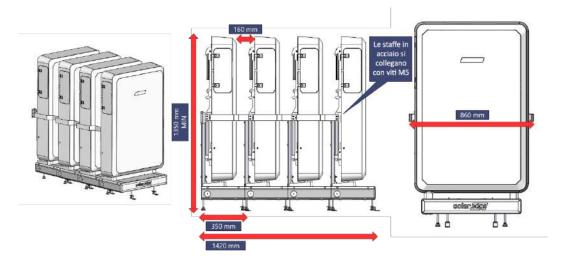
Disposizione dell'Energy Bank - Vista prospettica, laterale e frontale
